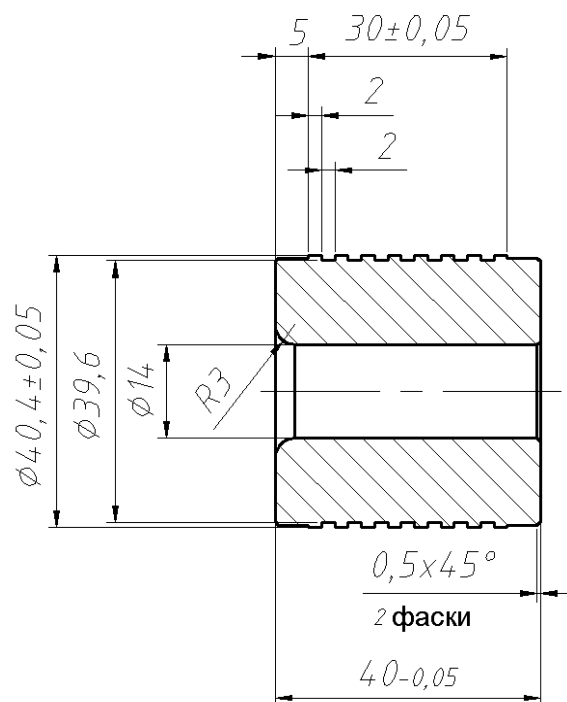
Эскиз втулки из твердого сплава ВК 20 с волнистым профилем.
